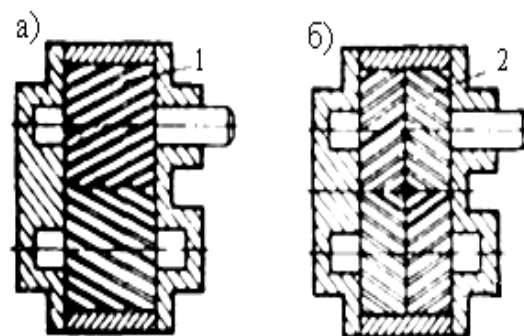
Насосы с косозубыми и шевронными шестернями
